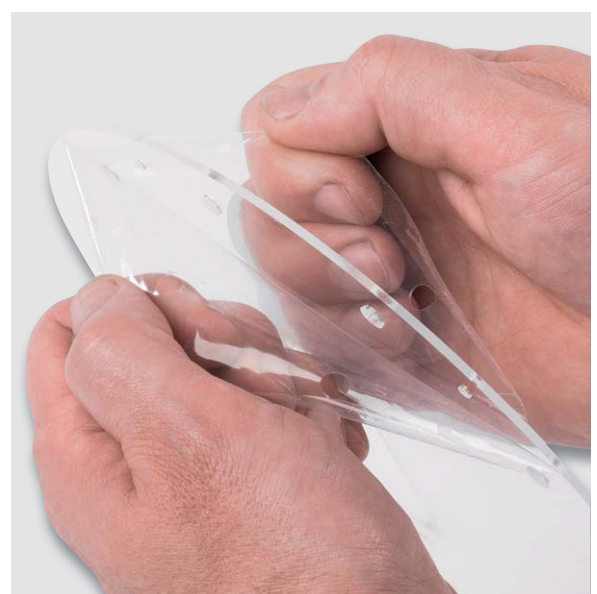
Vor der Montage der Abdeckscheibe sind die beidseitig aufgetragenen Schutzfolien zu entfernen.
